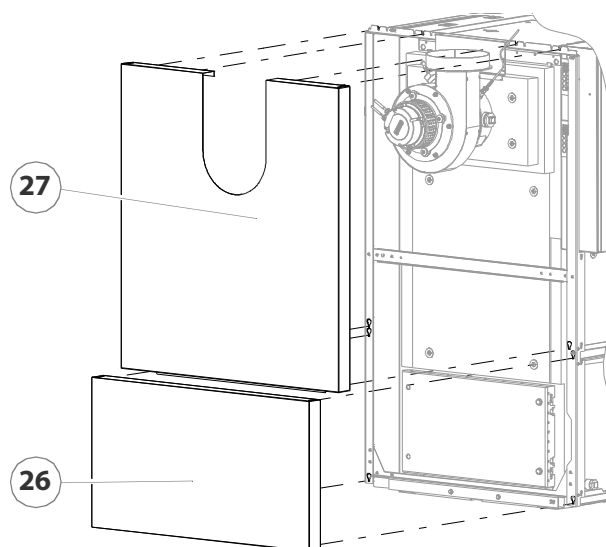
/29 - Montage du revêtement côté conduit de fumée
